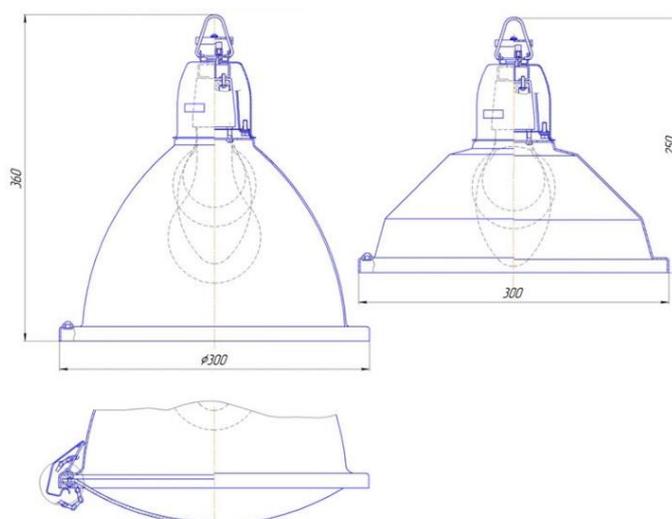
Габаритные размеры светильника НСП-26 (рис. из [23])
